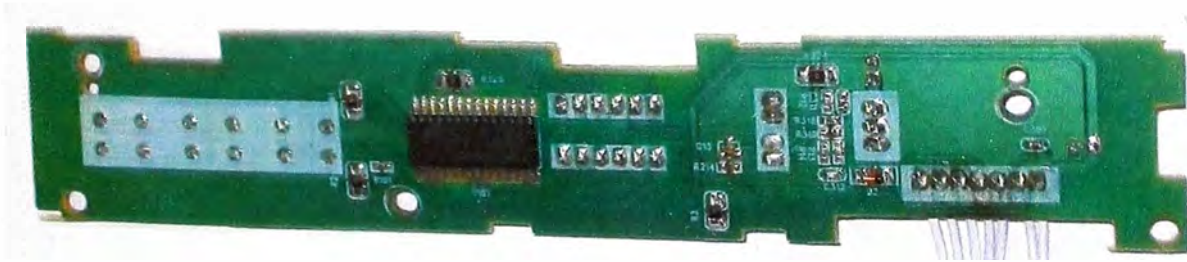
Placa PCB panel frontal (soldadura)
